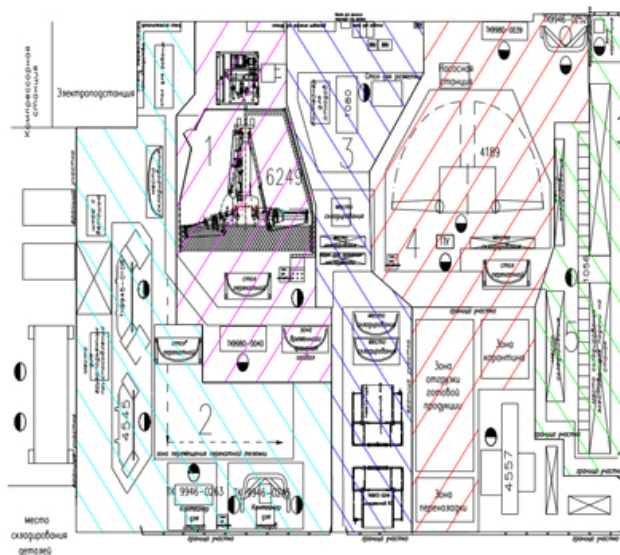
Пример схемы закрепления рабочих зон за исполнителями
